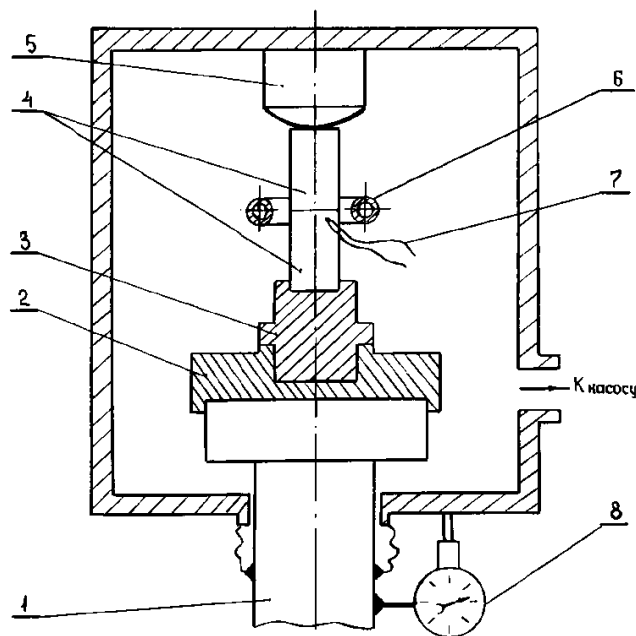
Схема установки для диффузионной сварки: 1, 5 – нижний (подвижный) и верхний штоки вакуумной камеры, соответственно; 2 – центрирующий фланец; 3 – вкладыш (сменный); 4 – свариваемые керамические образцы; 6 – индуктор; 7 – термопара; 8 – индикатор.
